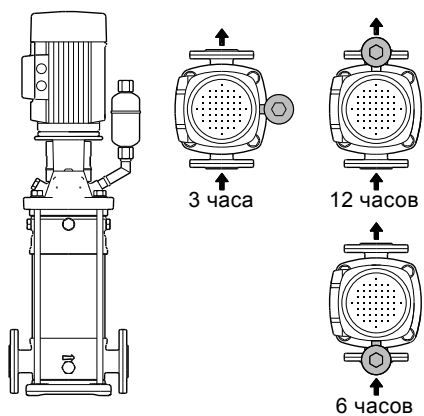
Расположение воздухоотводчика при вертикальном монтаже насоса CR
